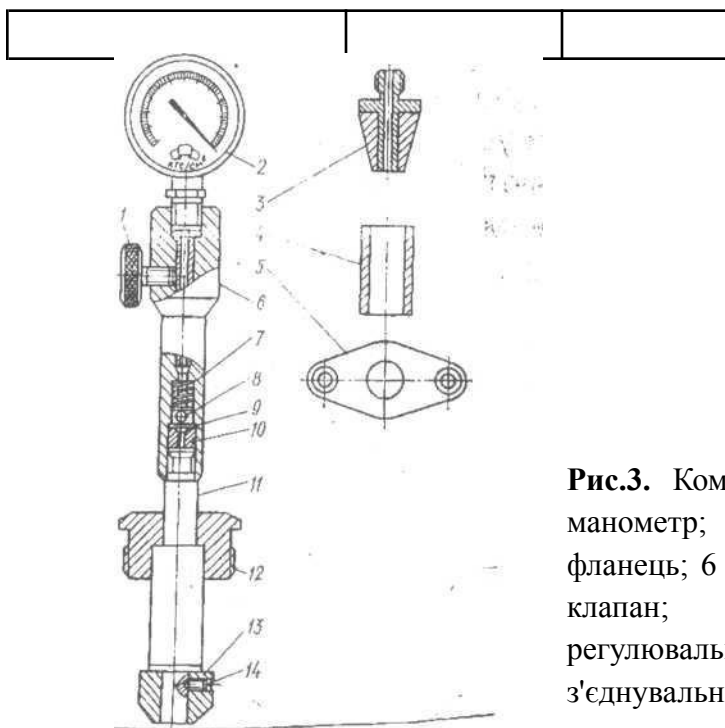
Компресиметр КИ-861: 1— вентиль; 2 — манометр; 3, 13 — наконечники; 4 — втулка; 5 — фланець; 6 — корпус; 7 — пружина; 8 — кульковий клапан; 9 — гумова прокладка; 10 — регулювальний гвинт; 11— трубка; 12 — з'єднувальна муфта; 14 — установочний гвинт.
